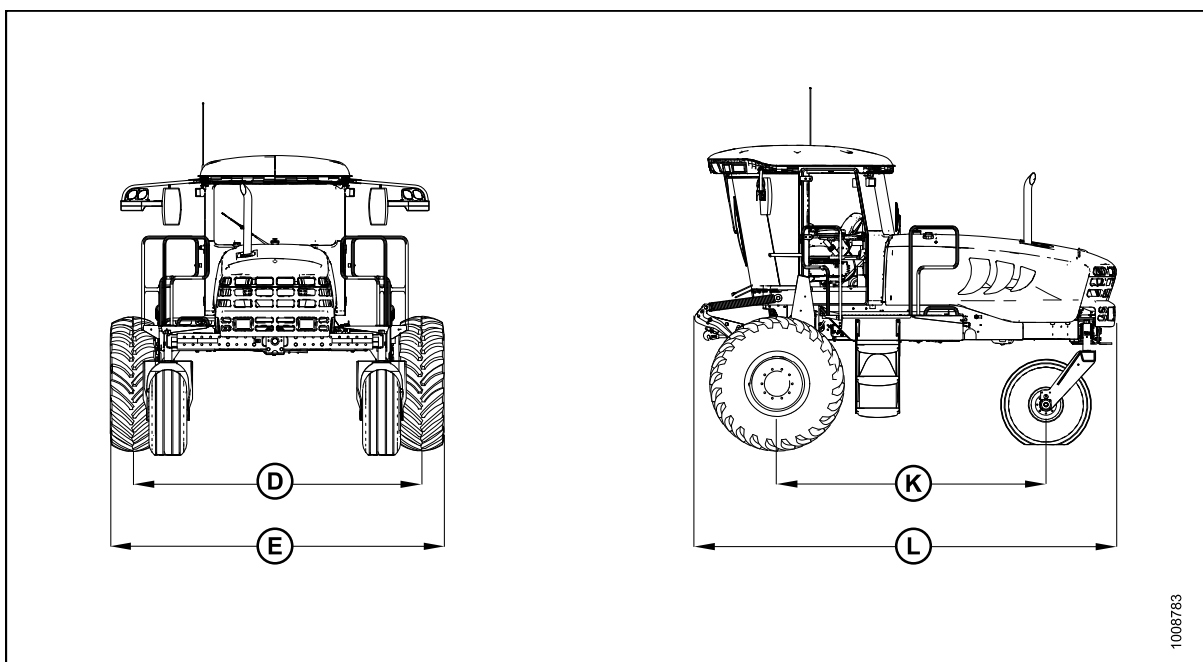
Размеры валковой косилки — Задняя часть
